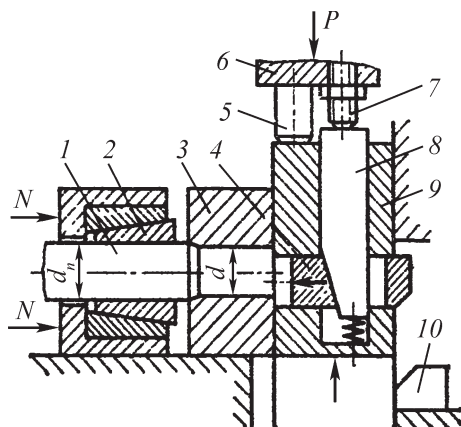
Принципиальная схема штампа-автомата для закрытой отрезки точных коротких заготовок
